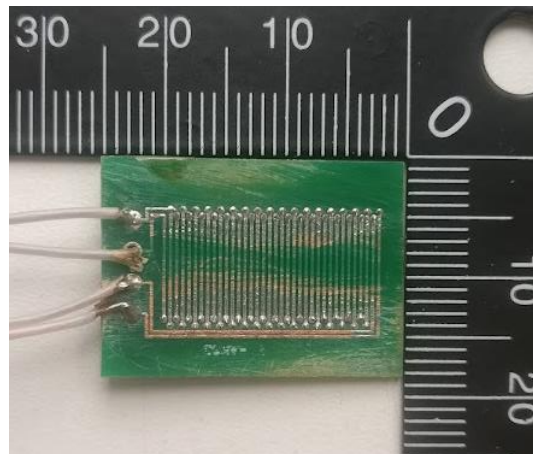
Изготовленный образец 5 RTD-феррозонда
